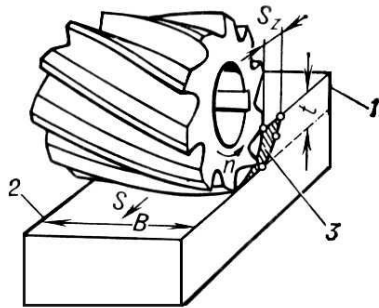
Схема резания при фрезеровании цилиндрической фрезой
